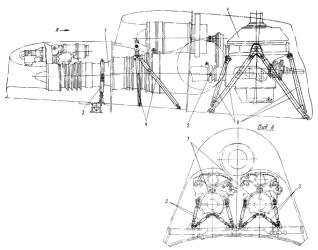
Схема крепления двигателей и редуктора на вертолете: I — двигатель; 2 — редуктор; 3 — стойки крепления двигателя в передней его части; 4 — приспособление для удержания двигателя при снятии редуктора с вертолета; 5 — сферическая опора редуктора для крепления двигателя в задней его части; 6 — подкосы рамы крепления редуктора
